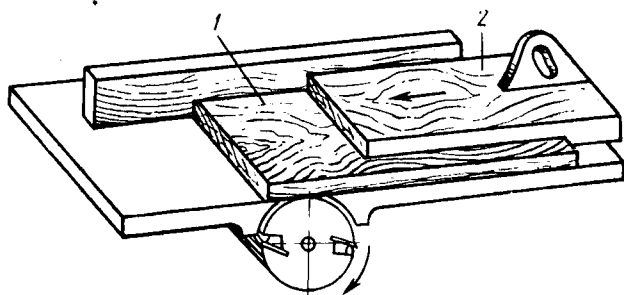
Приспособление для подачи на режущий инструмент коротких заготовок:
